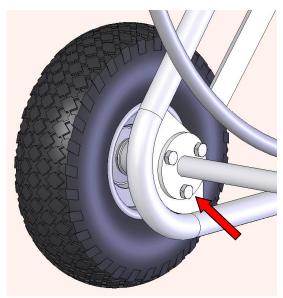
Radachsenbefestigung im Seitenrahmen integriert und mit Flanschverbindung verschraubt. Höhere Stabilität und schöneres, integriertes Design.
